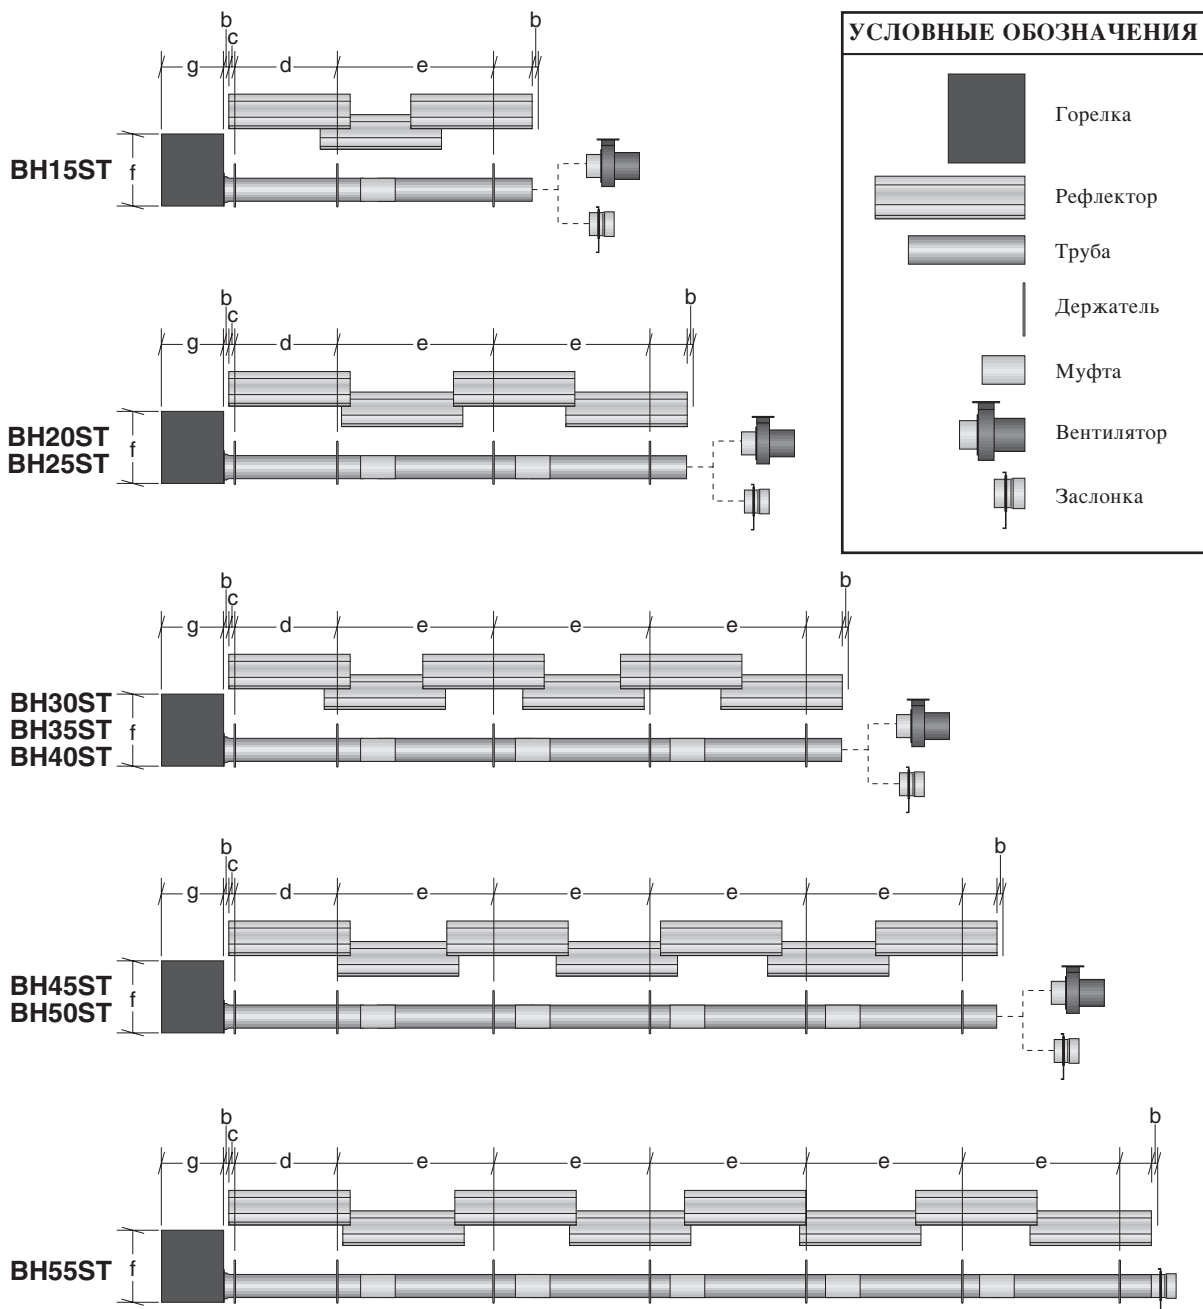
BLACKHEAT® Чертежи одинарного линейного обогревателя
